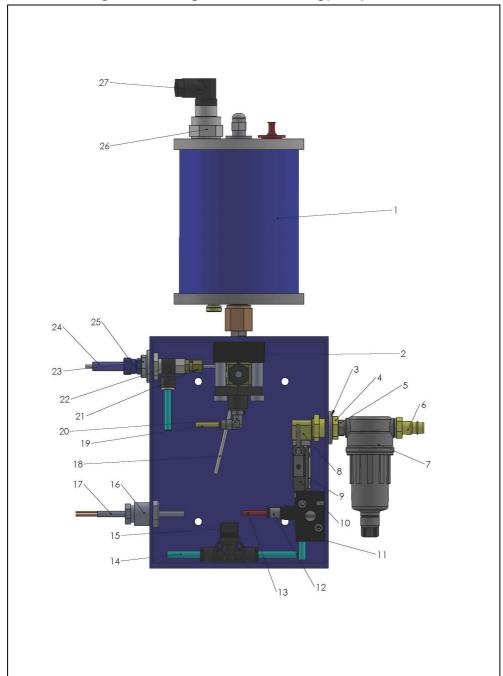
Ersatzteile Minimalmengenschmiergerät mit Messingpumpe
